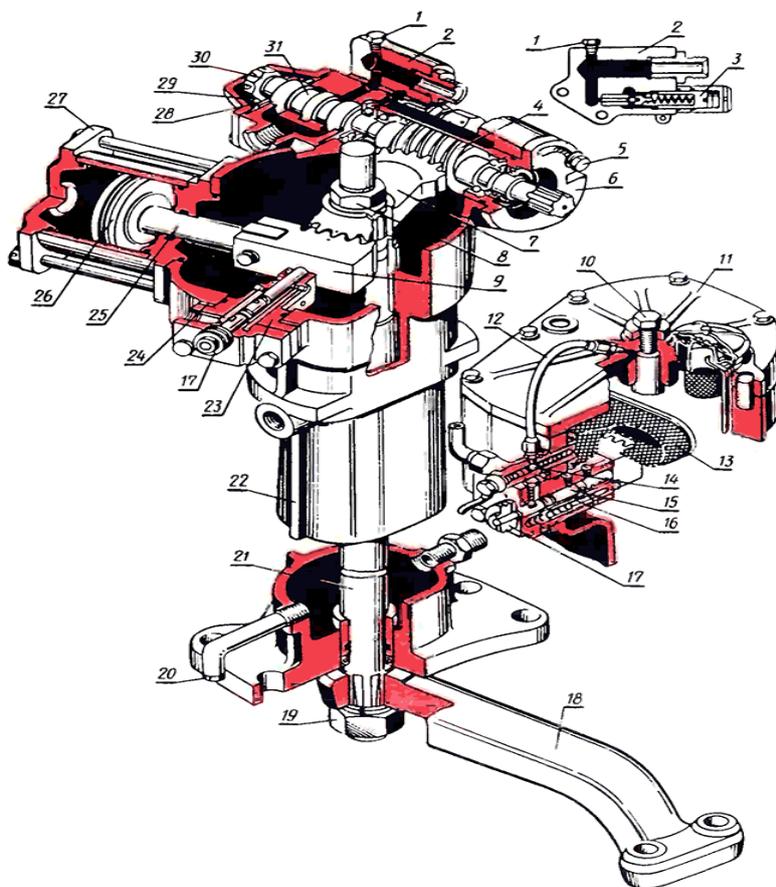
Гидроусилитель рулевого управления: 1 - пробка; 2 - клапанная крышка; 3 - регулировочный винт предохранительного клапана; 4 - червяк; 5 - болт регулировочной втулки; 6 - регулировочная эксцентричная втулка; 7 - сектор; 8 - гайка; 9 - рейка; 10 - регулировочный винт; 11 - верхняя крышка; 12 - маслопровод смазки верхней опоры; 13 - фильтр; 14 - редукционный клапан; 15 - кран управления; 16 - золотник датчика; 17 - маховичок крана; 18 - сошка; 19 - гайка; 20 - сливная пробка; 21 - поворотный вал; 22 - корпус; 23 - упор рейки; 24 - регулировочные прокладки; 25 - шток; 26 - поршень; 27 - передняя крышка цилиндра; 28 - упорный подшипник; 29 - крышка; 30 - гайка; 31 - золотник.
